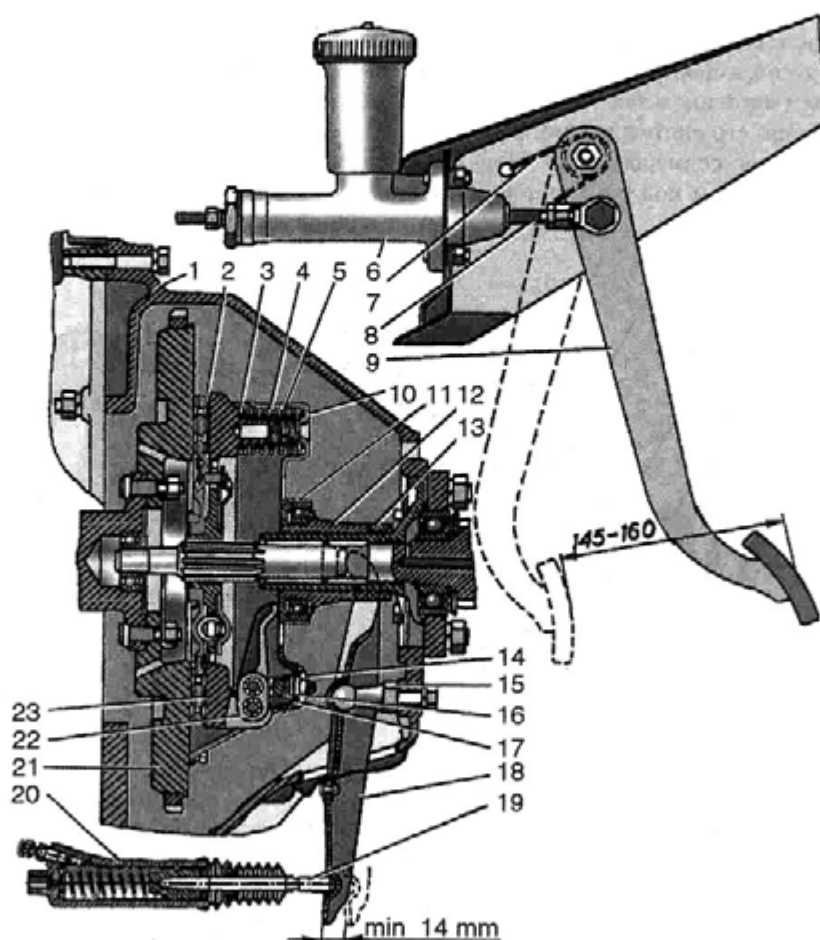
Сцепление рычажного типа и привод выключения сцепления:
